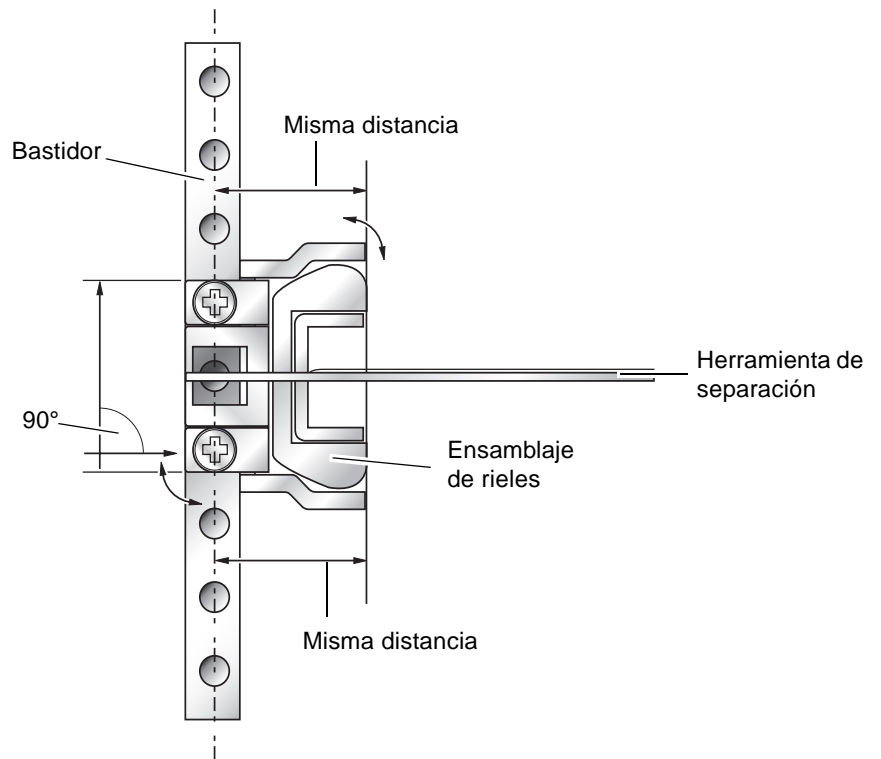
Colocación de la herramienta de separación (vista en planta)
